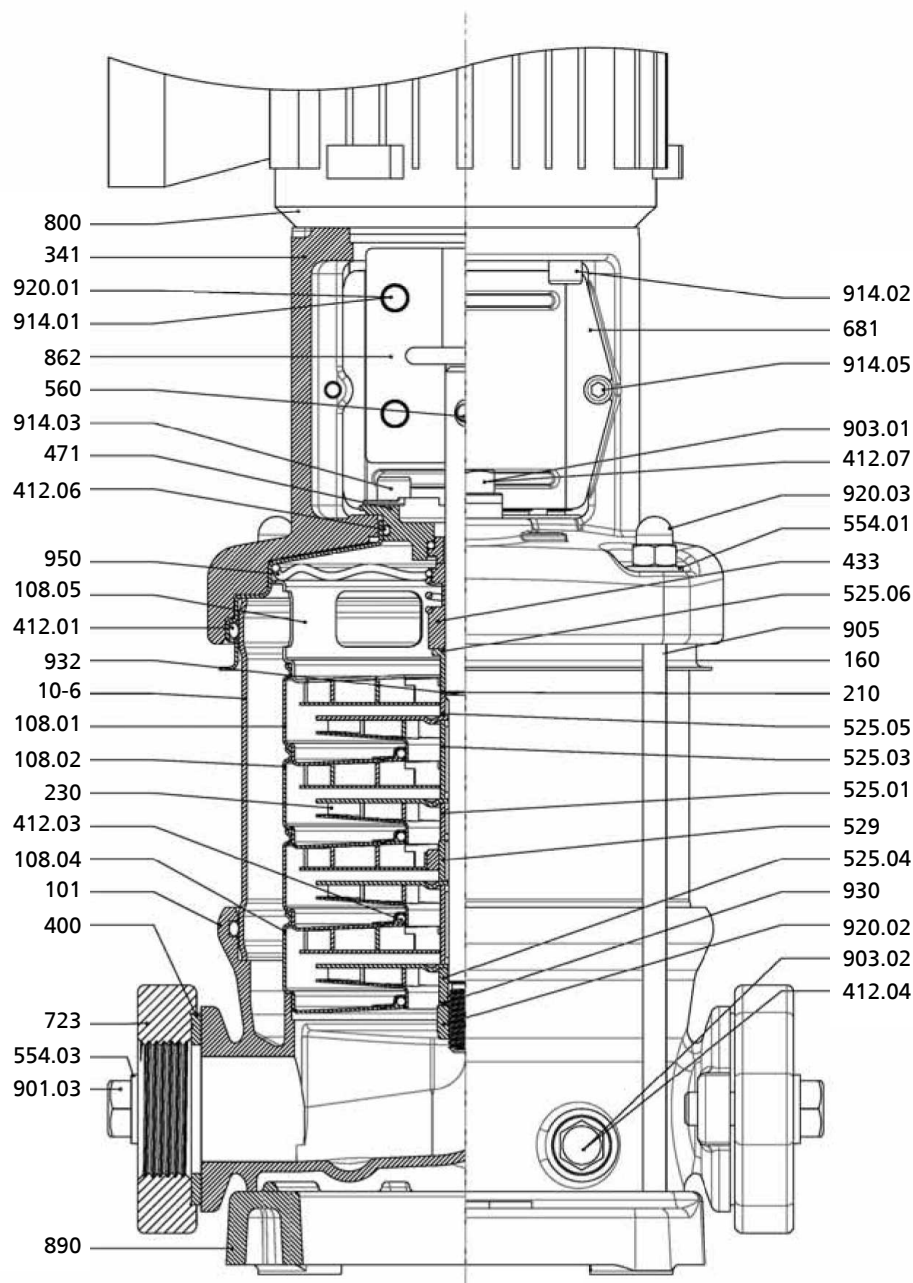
Обзорный чертеж Movitec V 2, 4, 6
